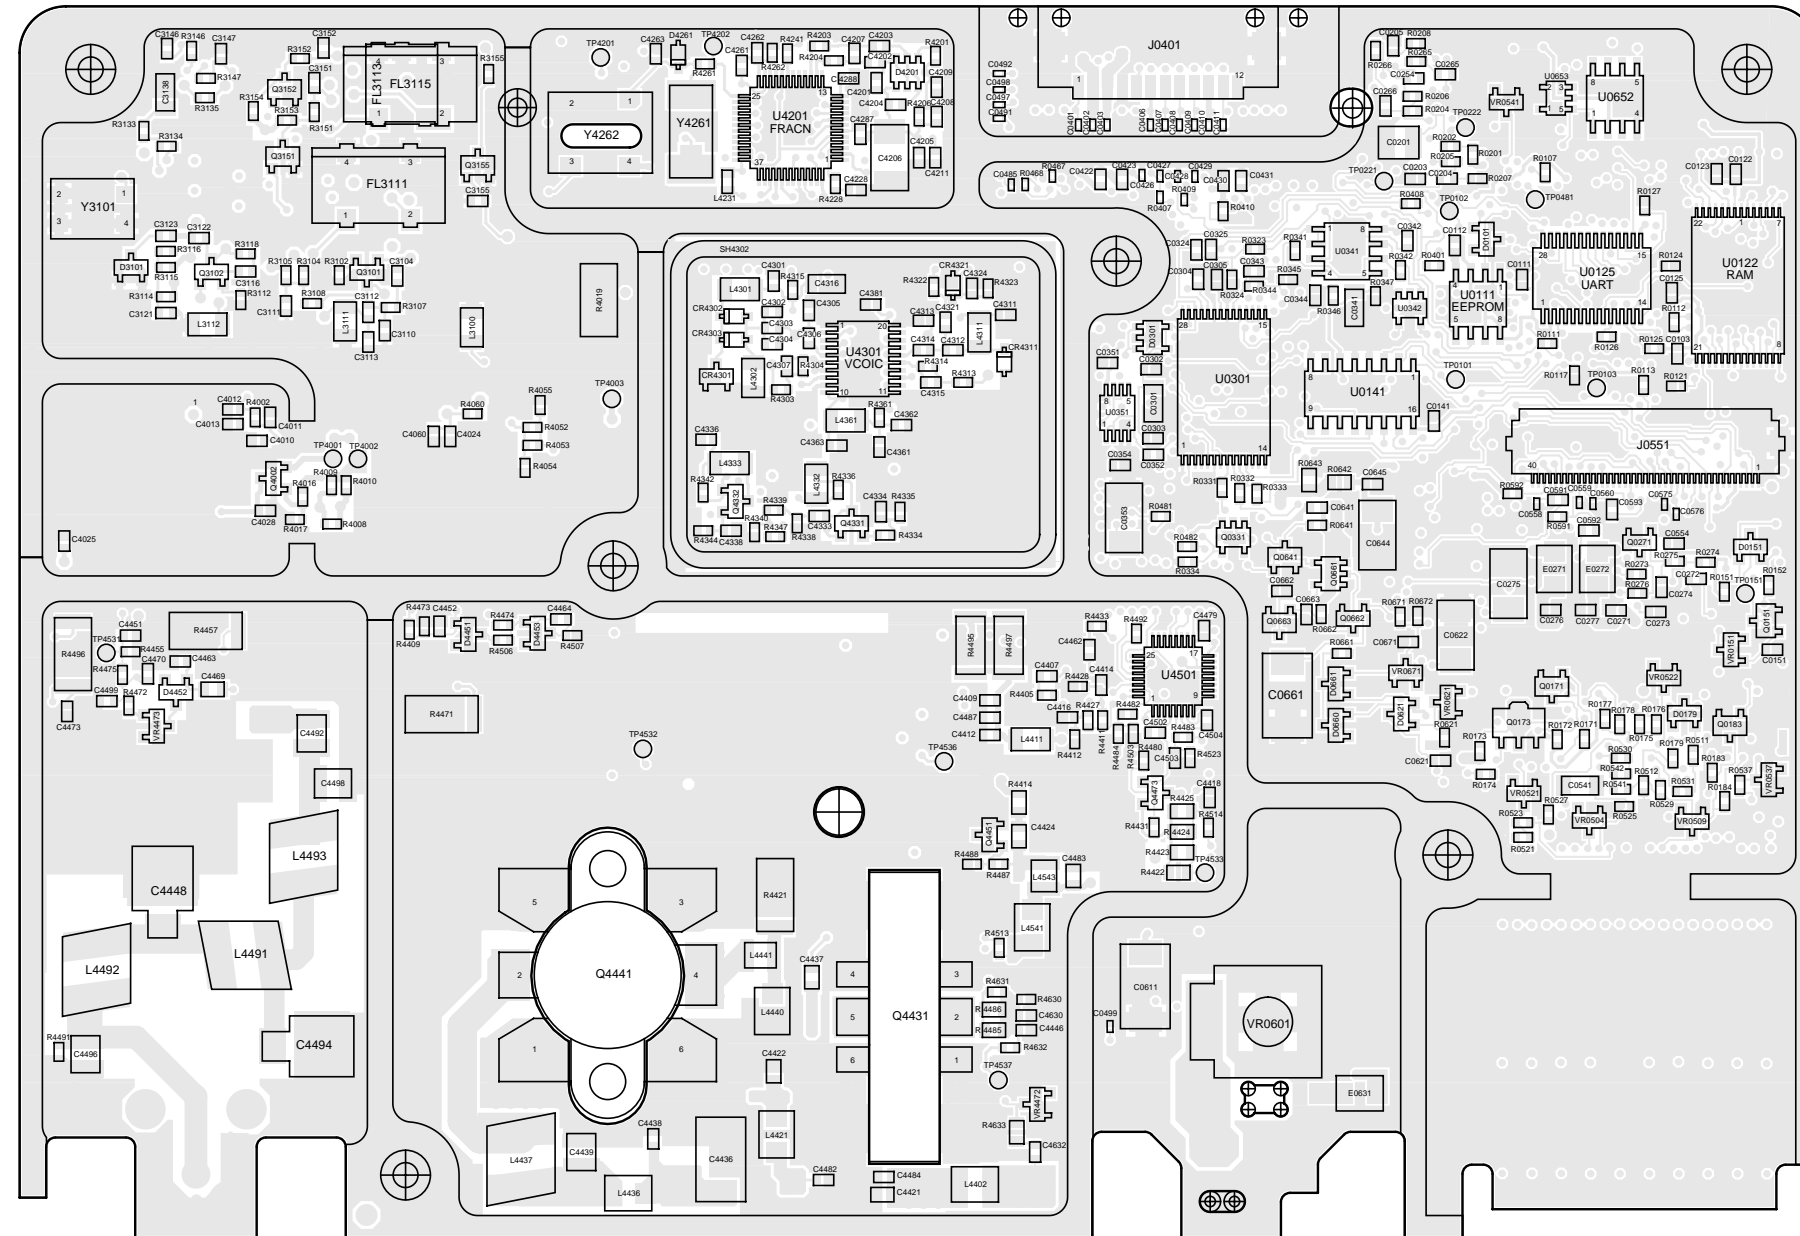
PCB del lado inferior de la tarjeta principal de UHF (403-470MHz)
